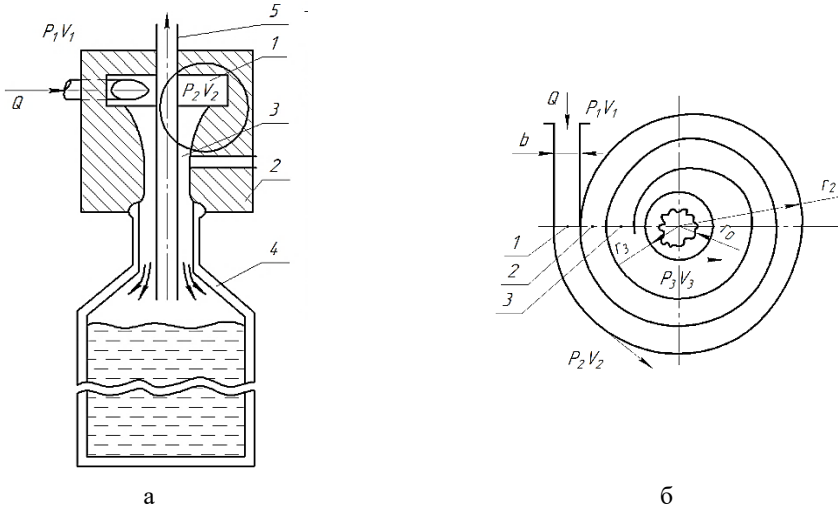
Дозатори прямої дії з потоком рідини, яка обертається: а — схема розливної головки; б — канали руху рідини; 1 — камера розливної головки; 2 — корпус дозатора; 3 — канал подачі рідини; 4 — споживча тара; 5 — трубка для виходу повітря
